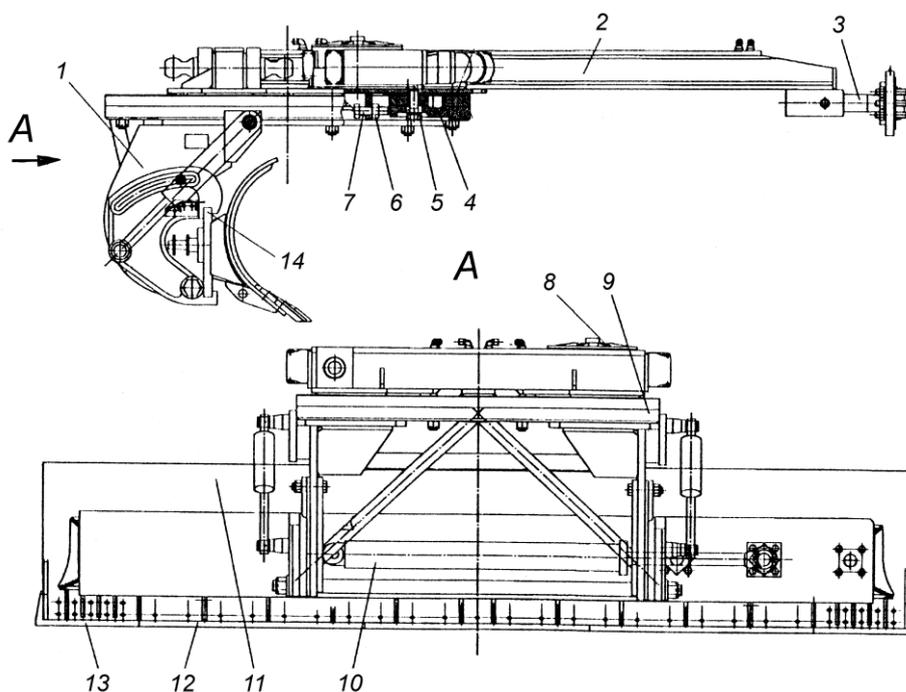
Грейдерный отвал автогрейдера ДЗ-298: 1 – кронштейн изменения угла резания; 2 – тяговая рама; 3 – шкворень; 4 – накладка; 5 – болт; 6 – контргайка; 7 – регулировочный болт; 8 – редуктор поворота отвала; 9 – поворотный круг; 10 – гидроцилиндр выноса отвала; 11 – отвал; 12 – основной нож; 13 – боковой нож; 14 – сменный вкладыш
